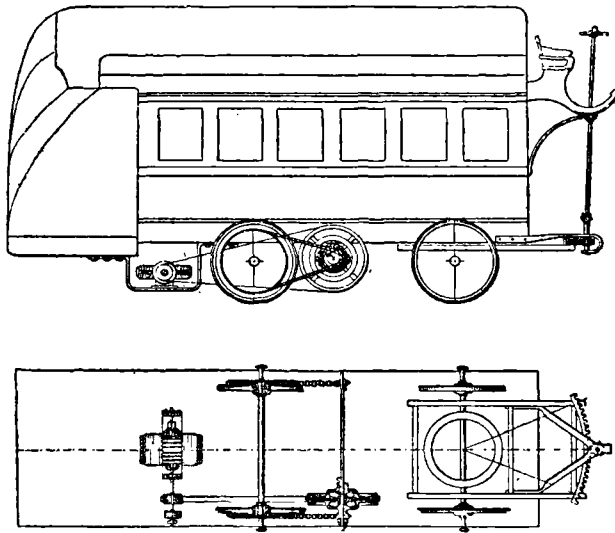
Elévation et plan de la voiture d'essai à accumulateurs de M. Raffard.
